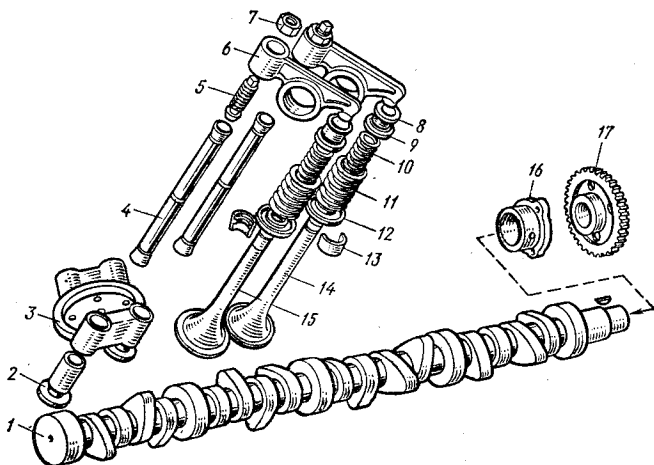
Деталі механізму газорозподілу (КамАЗ-740):
